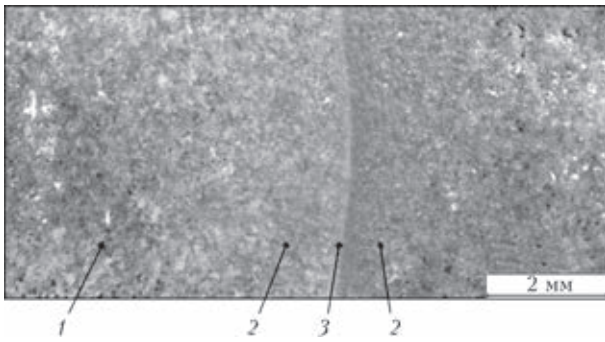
Макроструктура сварного соединения заготовки из спеченного титана ВТ1-0, полученной сваркой трением: 1 — основной металл; 2 — околошовная зона; 3 — шов
